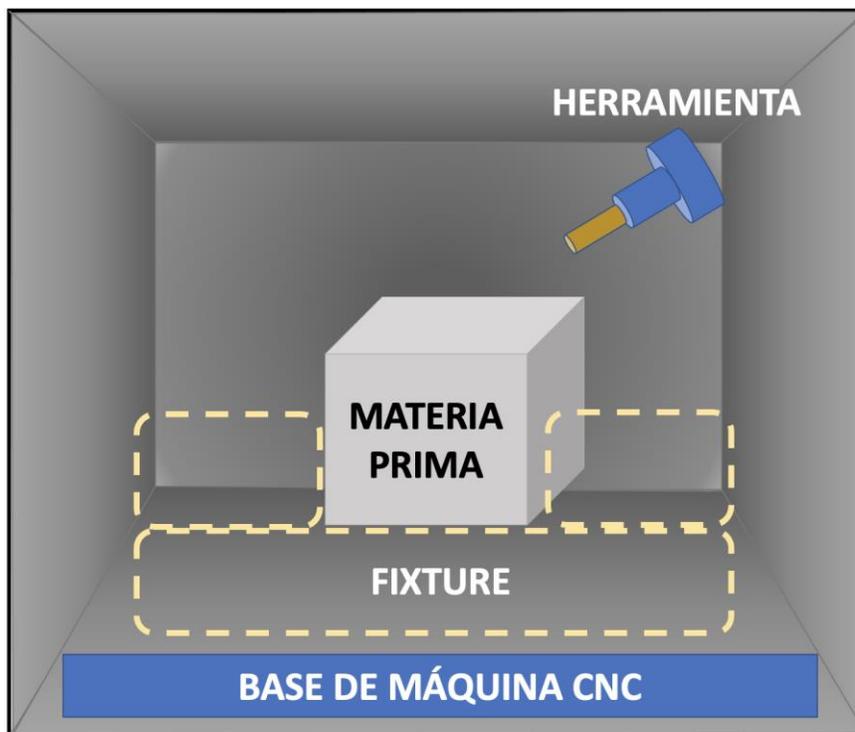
Interior de una maquina CNC con Fixture y Materia Prima.
